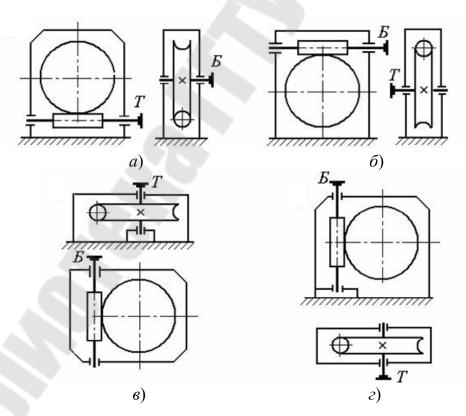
Кинематические схемы одноступенчатых червячных редукторов
